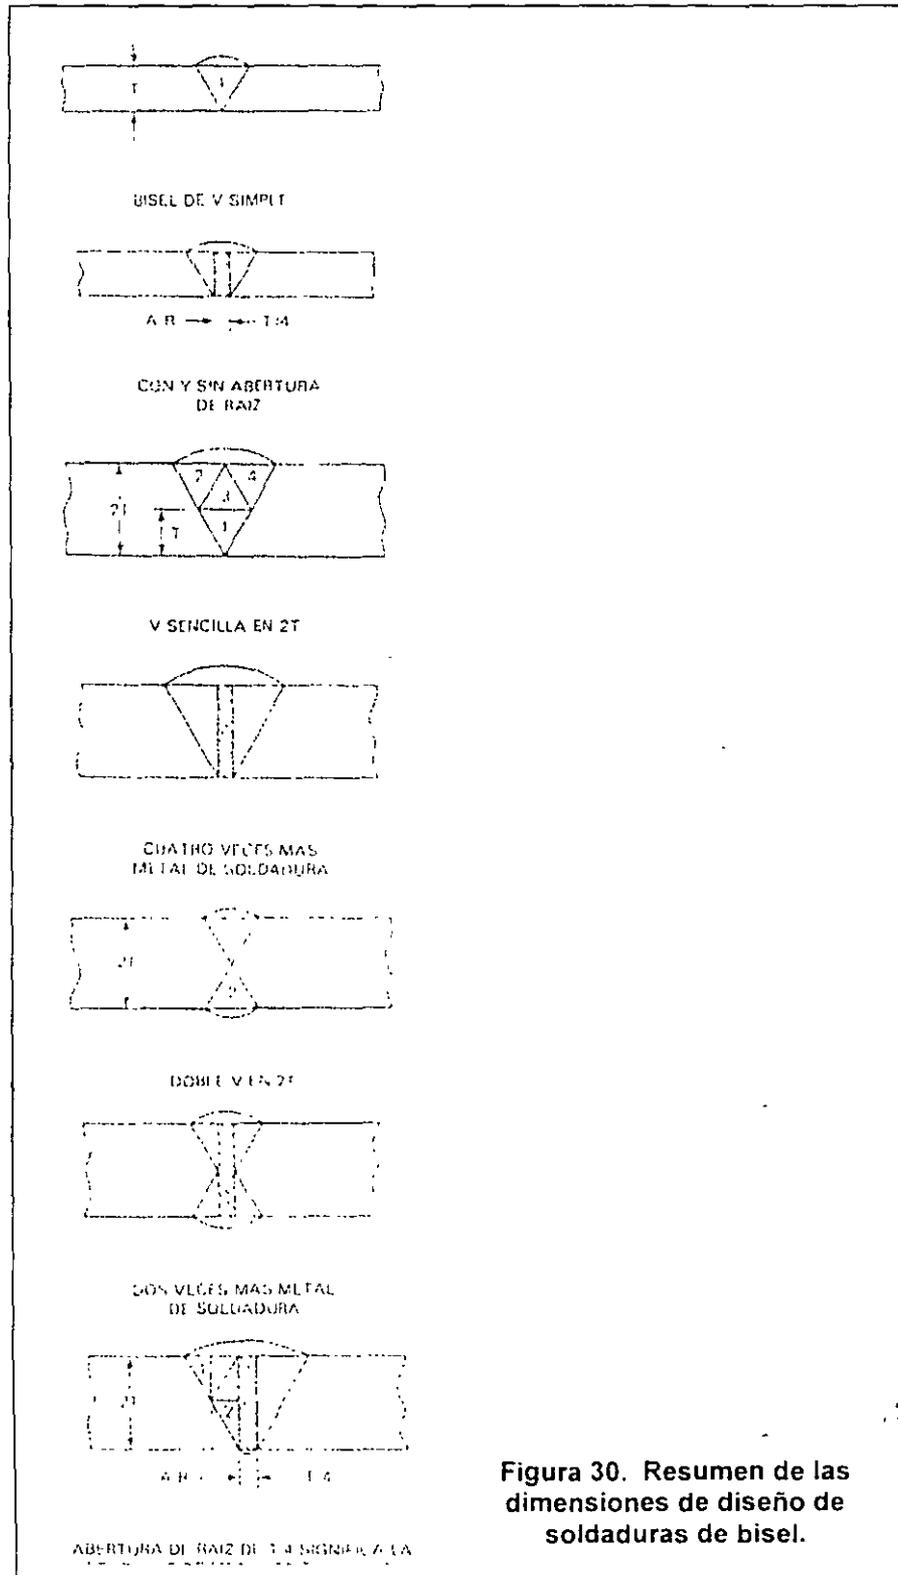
Resumen de las dimensiones de diseño de soldaduras de bisel.
